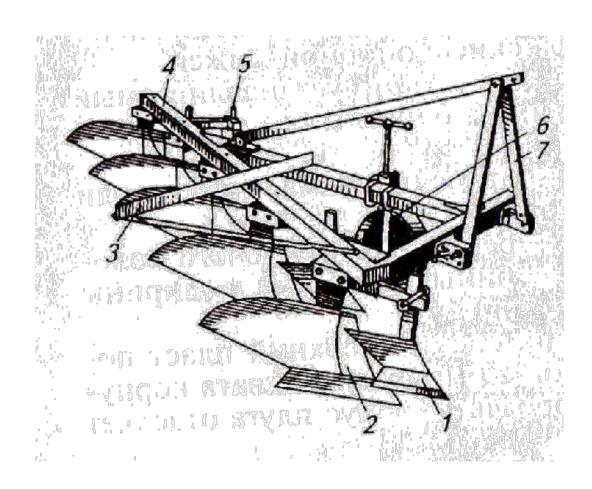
Навесной плуг ПЛН -5 -35: 1 — предплужник; 2 —корпус; 3 — прицеп для бороны; 4 — рама; 5 — дисковый нож; 6 — опорное колесо; 7 — навеска.
